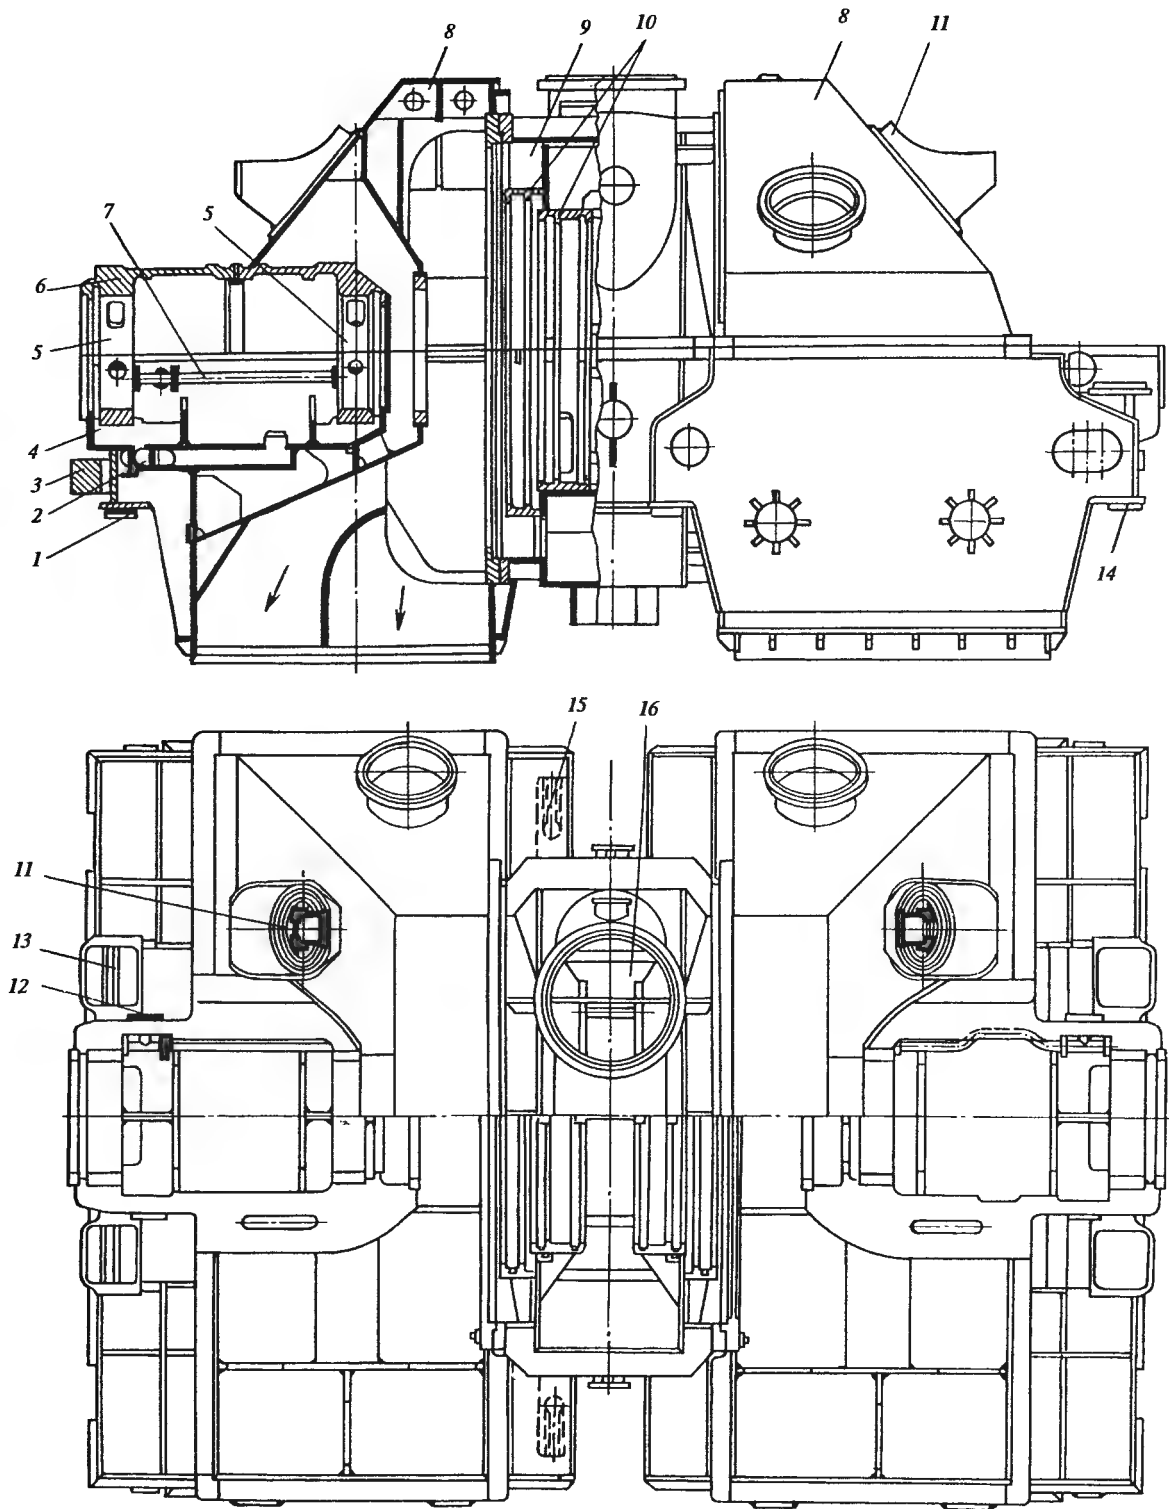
Конструкция одностенного корпуса ЦНД
